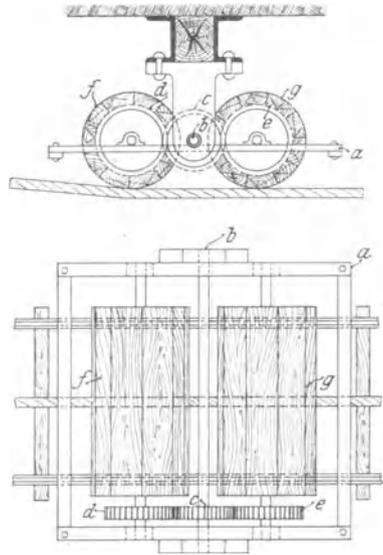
Druckrolle für Förderung mit Kettchenanschlag.
